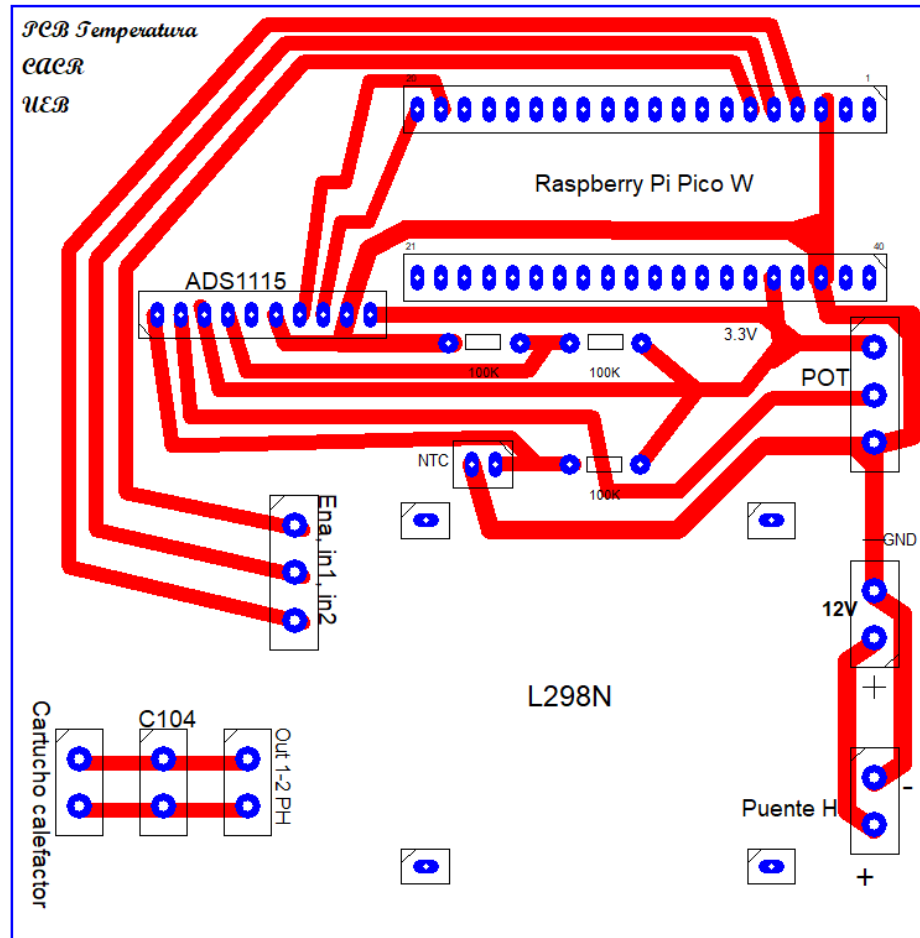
Diagrama PCB elaborado en PCB Wizard.
